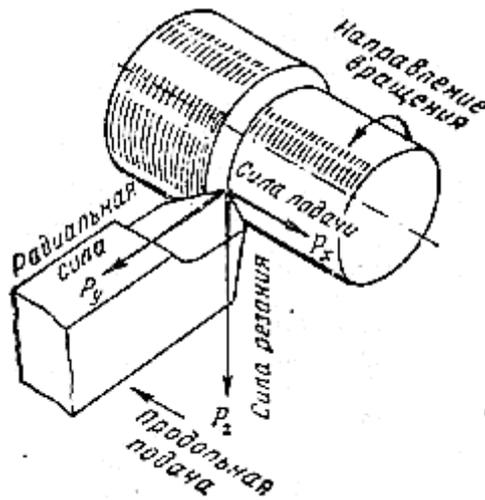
Силы, действующие на резец в процессе токарной обработки
